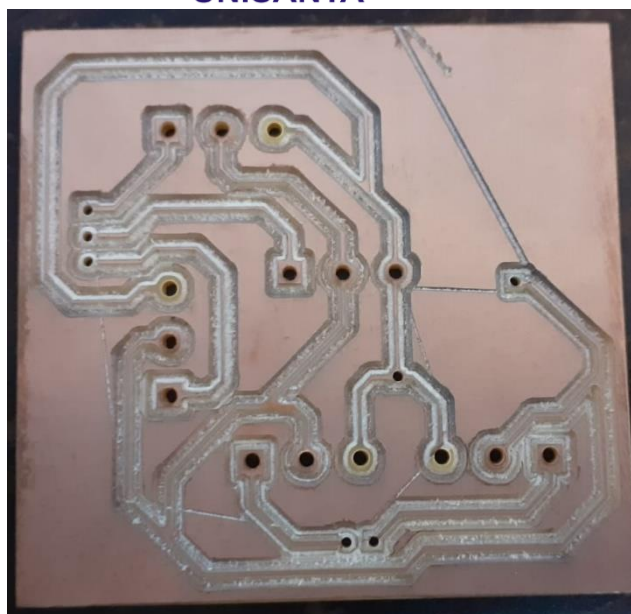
PCB 1 que sofreu com defeitos da prototipadora
